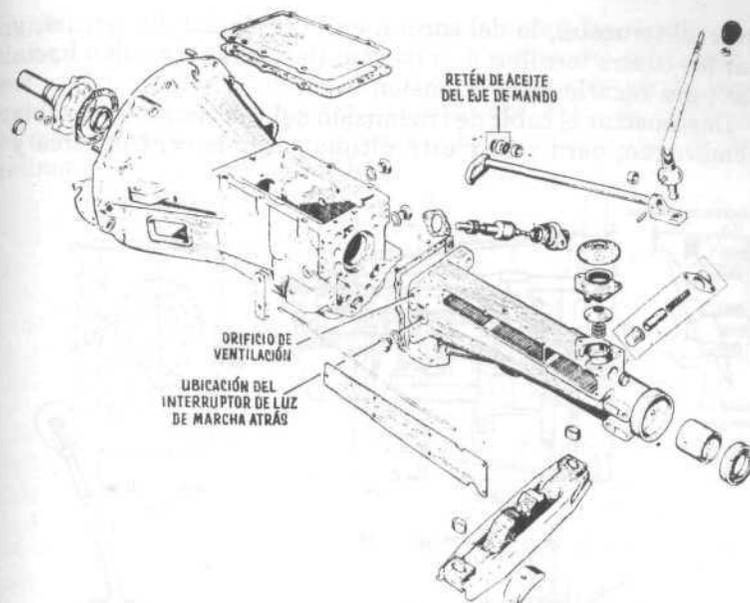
Componentes de la caja, la extensión y la palanca de cambios.
